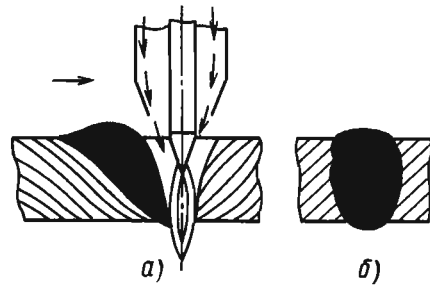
Схема сварки погруженной дугой (а) и форма проплавления в поперечном сечении шва (б)
